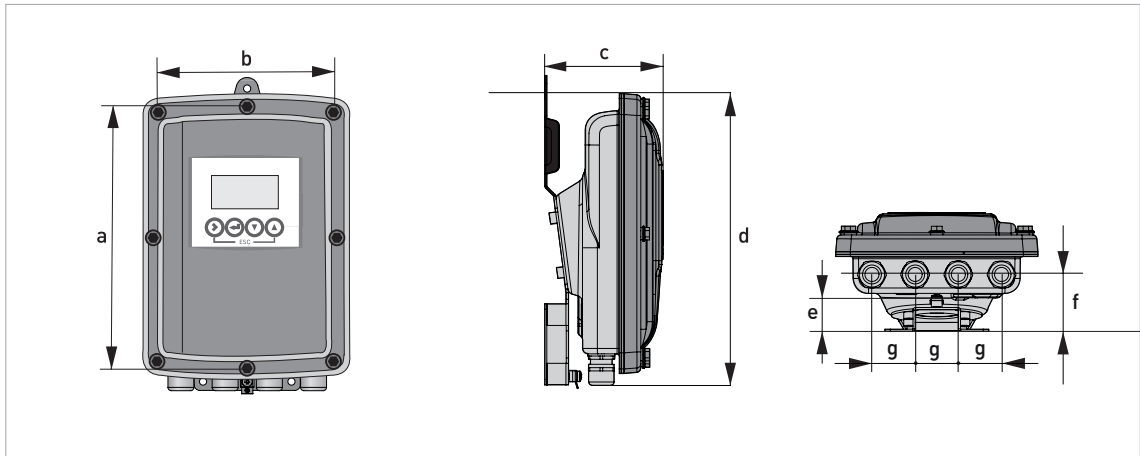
Размеры корпуса для настенного монтажа и компактного исполнения из нержавеющей стали (версия 10°)
